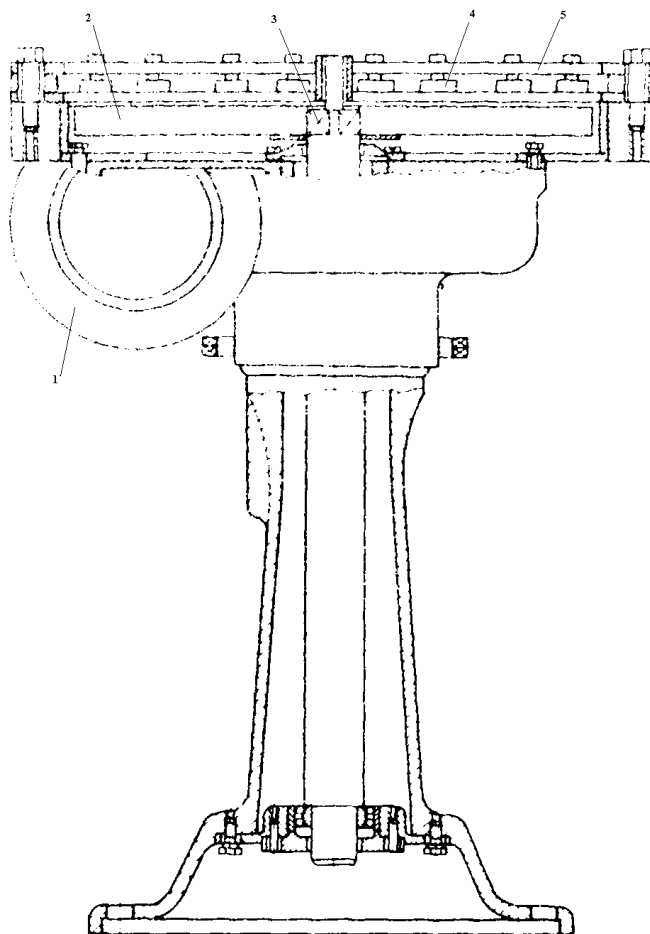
Приспособление для притирки тарелок, седел и шиберов.
